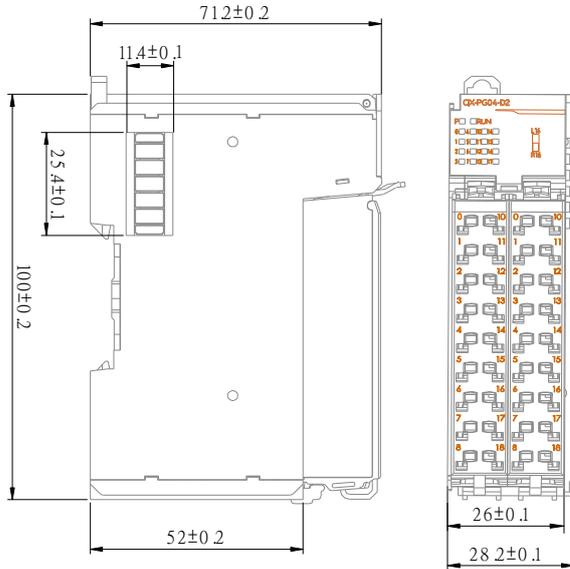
HCQX-PG04-D2 安装尺寸图 (单位: mm)
